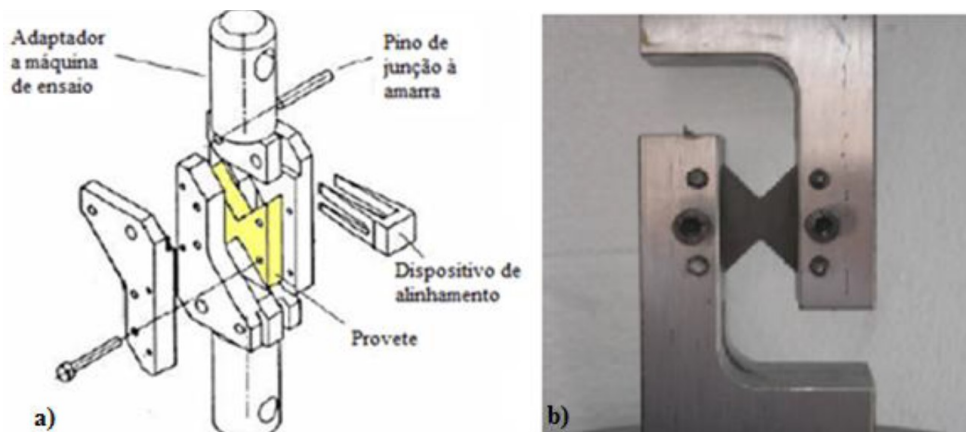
Figura 30 - Método Arcan [43] a) vista explodida e b) fixação [30]
